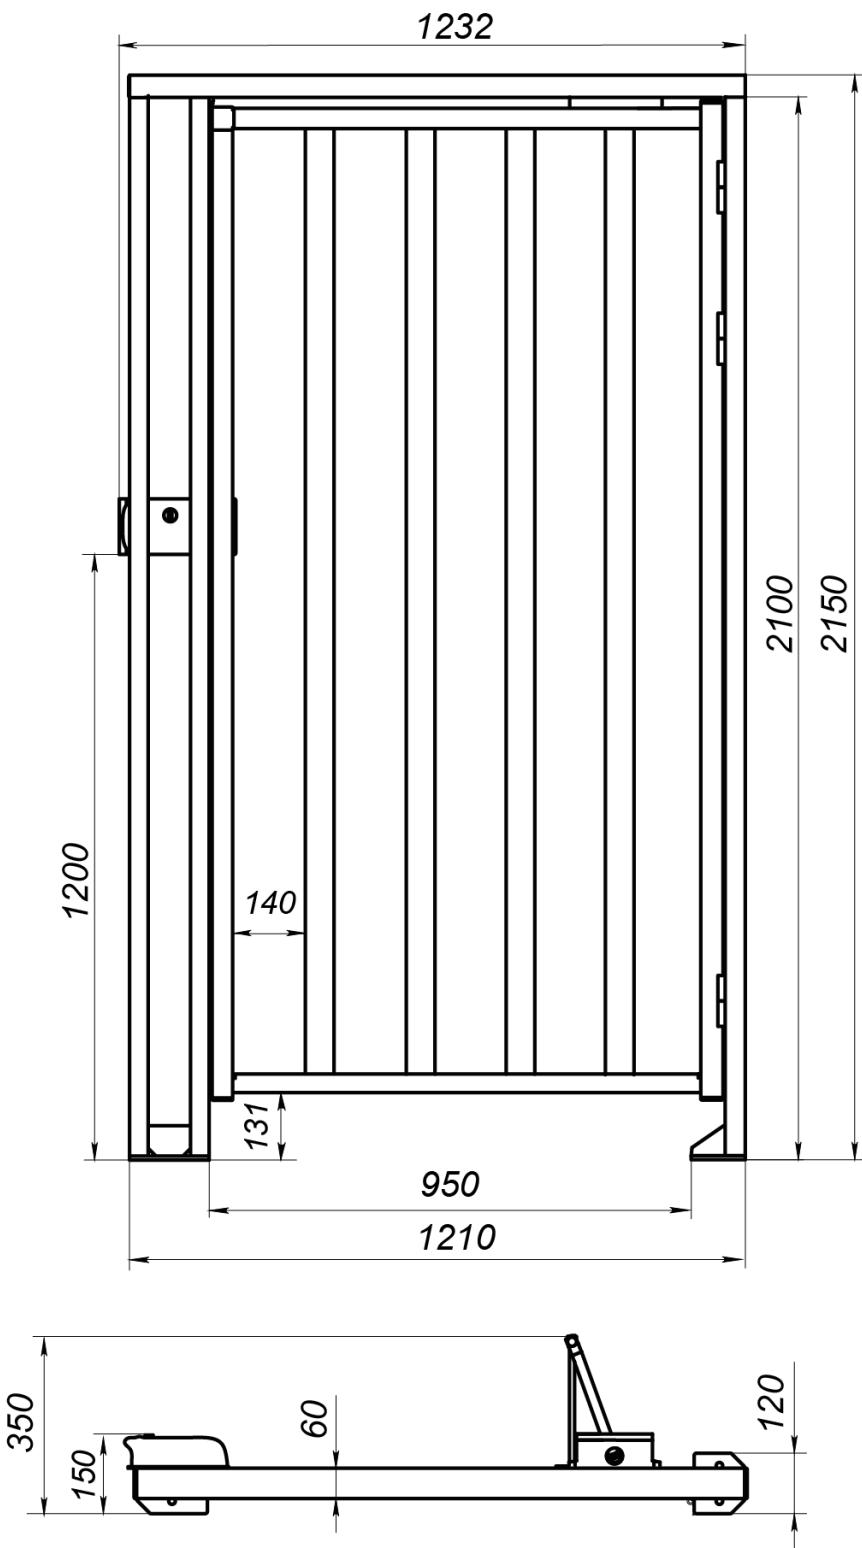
Габаритные и промежуточные размеры калитки PERCo-WHD-15
